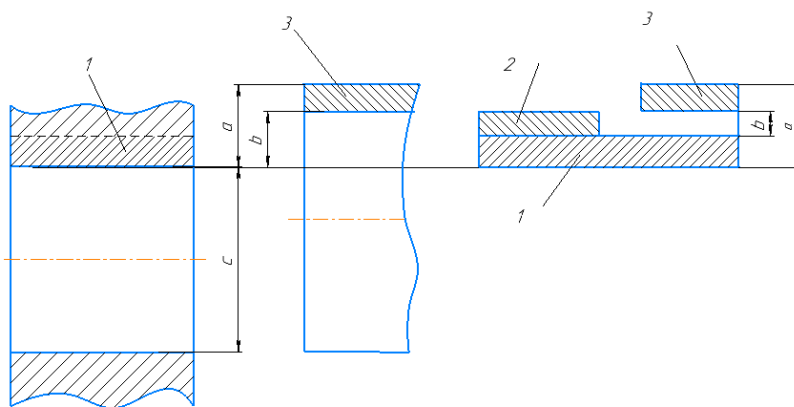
графическое представление посадки натягом: 1- интервал допуска отверстия; 2– интервал допуска вала; случай 1 – нижний предельный размер вала совпадает с верхним предельным размером отверстия, наименьший натяг равен нулю; 3 - интервал допуска вала, случай 2: нижний предельный размер вала больше, чем верхний предельным размером отверстия, наименьший натяг больше нуля; a – наибольший натяг; b – наименьший натяг; c – номинальный размер, равный нижнему предельному размеру отверстия
